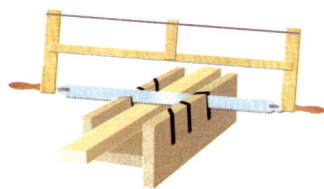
Пиление заготовки в стусле столярной ножовкой
